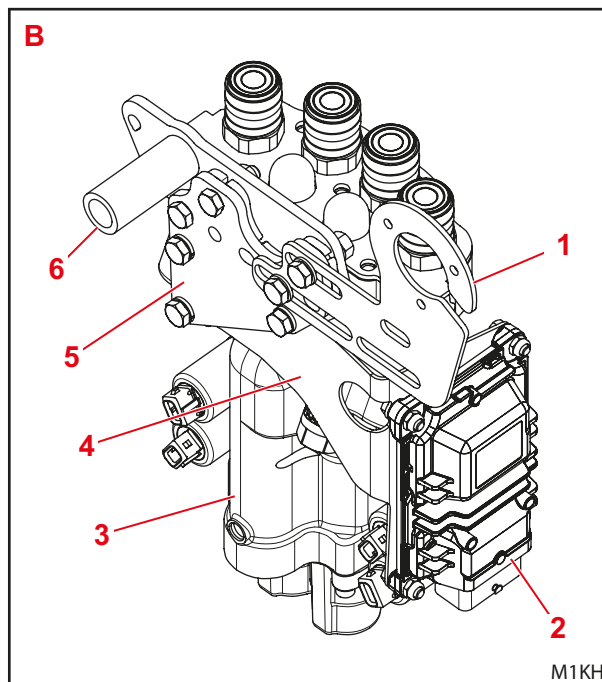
Montar a válvula proporcional (posição de montagem B)
